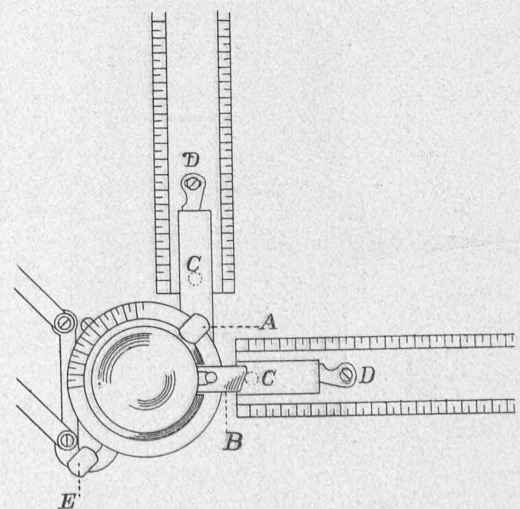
Schéma du mécanisme du « dessinateur universel ».
